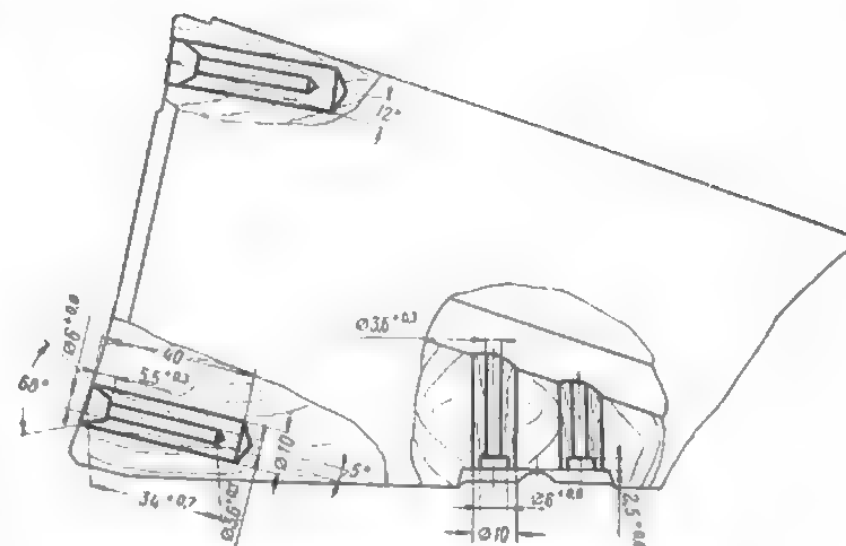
Обработка отверстия для шурупов в прикладе ложи
